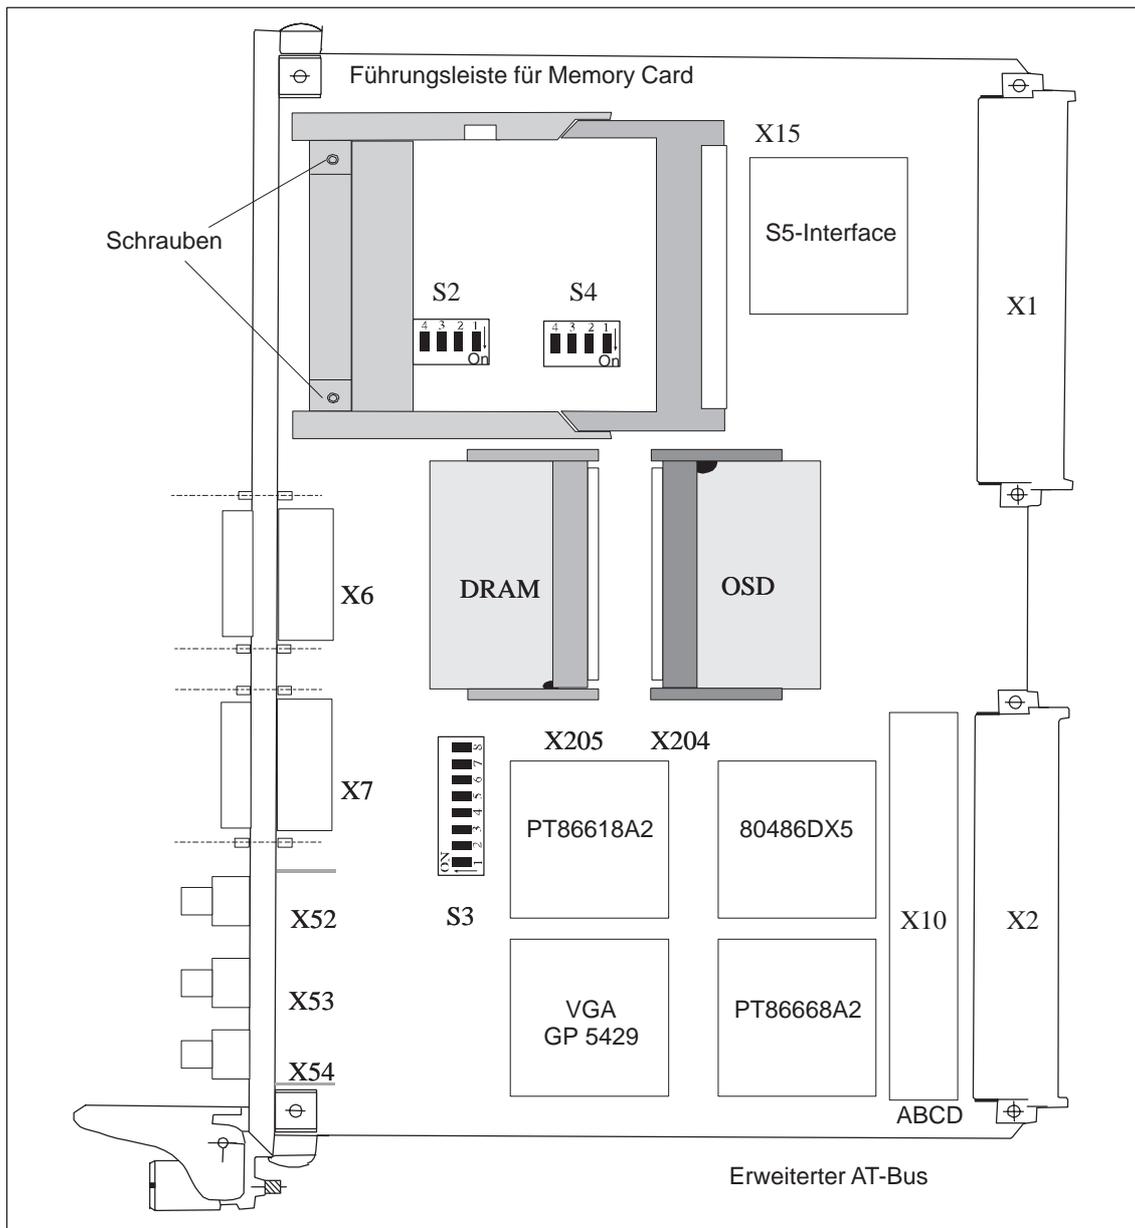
Aufbau der CP 581 Grundbaugruppe (80486 DX)
